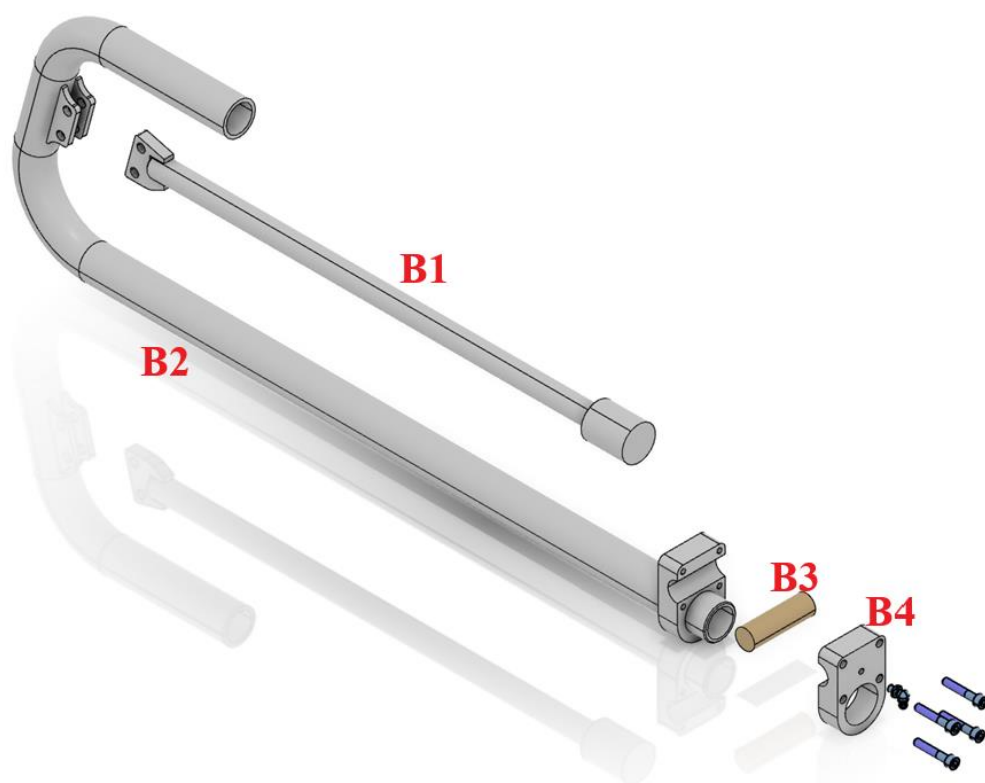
Cylindermodul i sprängd presentation med komponentnumrering.
